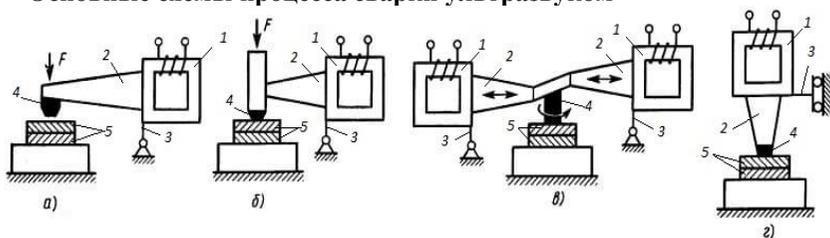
Основные схемы типовых установок для УЗС металлов: а) продольная; б) продольно-поперечная; в) продольно-вертикальная г) крутильная [3].
